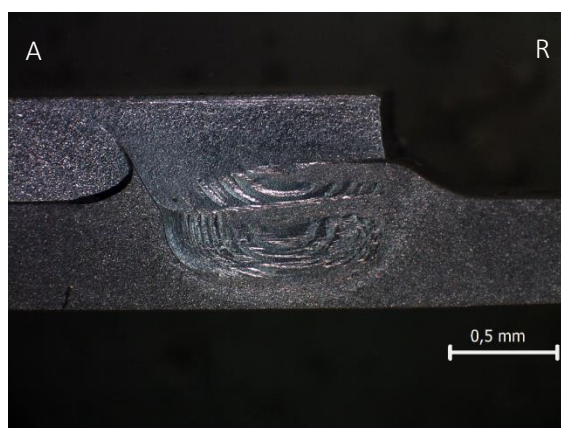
Macroestrutura de uma junta de FSW sujeita a um ensaio de tração.
